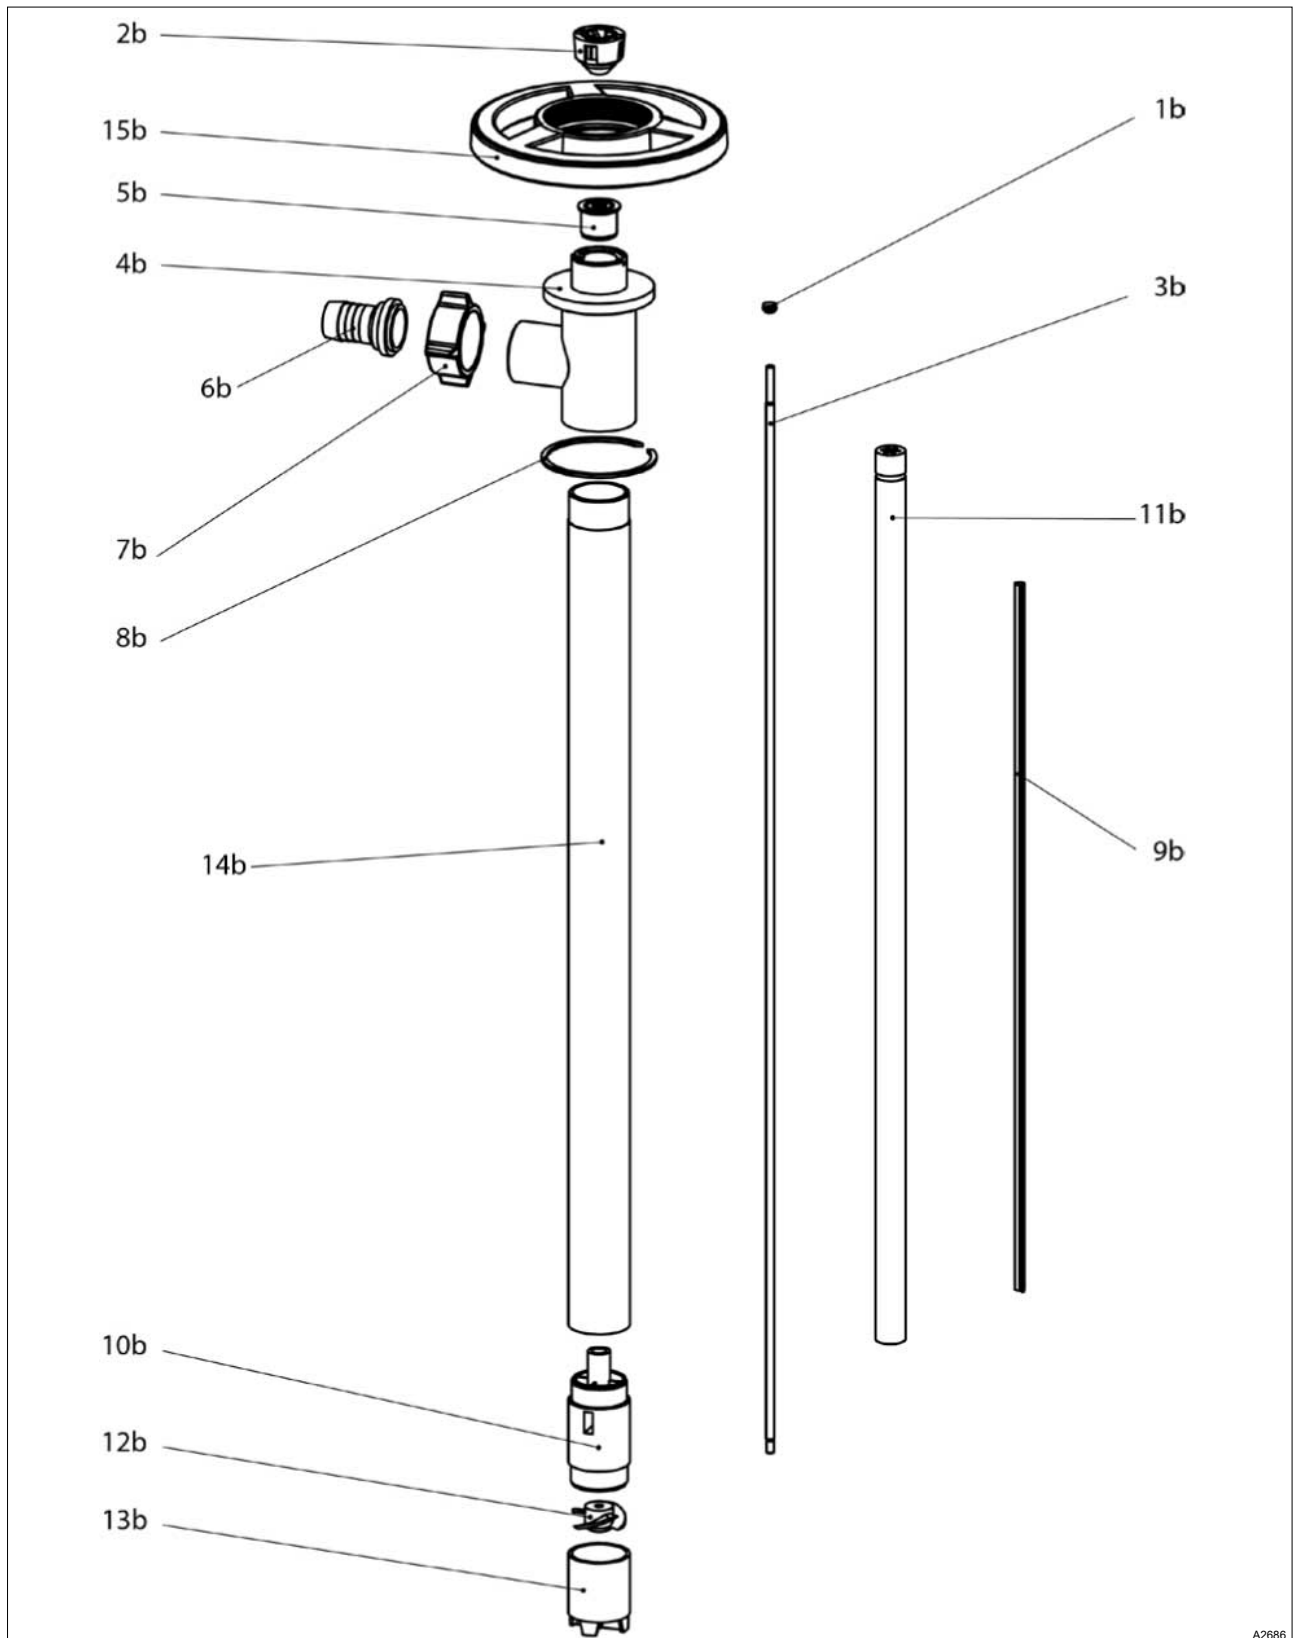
Ersatzteilzeichnung für die Pumpe.
